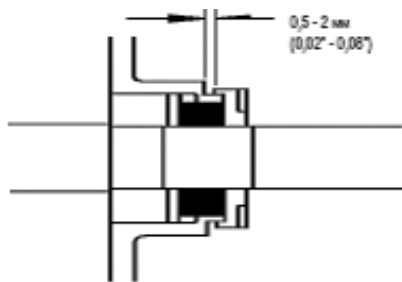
(Установка зазора между дефлектором и корпусом)
